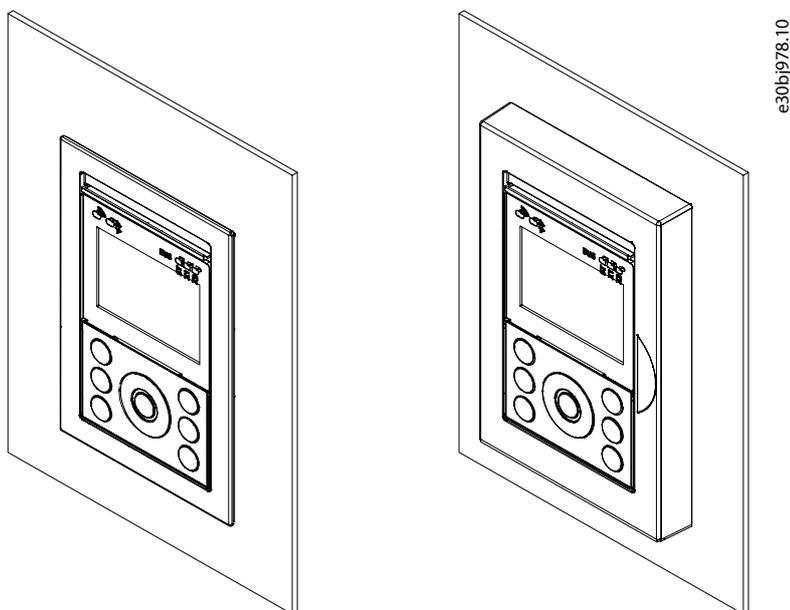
Panneau de commande monté dans le kit de montage aligné (gauche) et le kit de montage panneau sur porte (droite)
